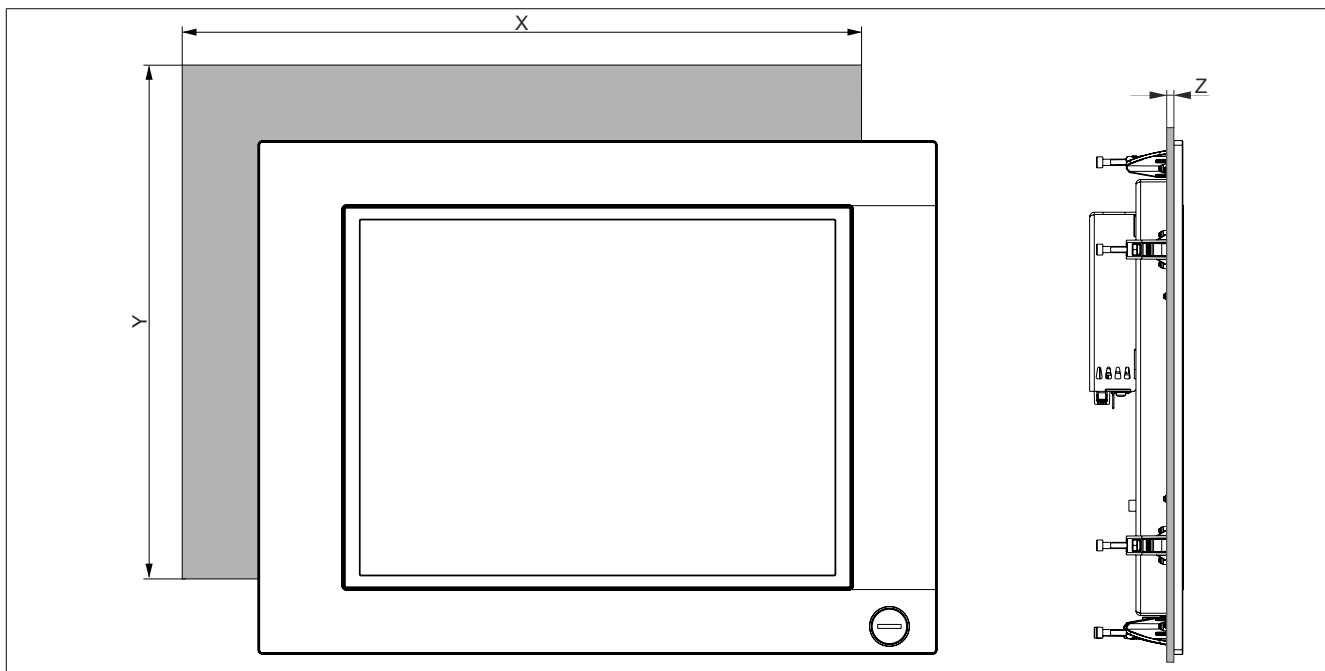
Einbauzeichnung - Panel PC 2100 mit AP1000 Panels mit Klemmblöcken (Beispielabbildung)
